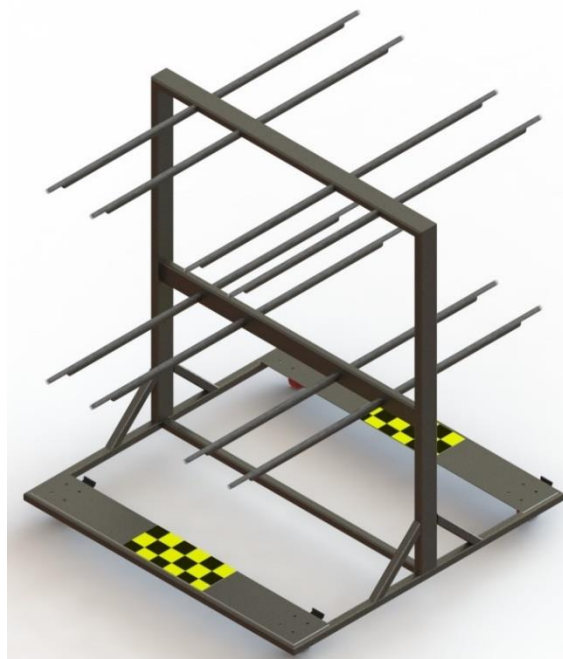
Esboço final da estrutura metálica para paletização dos painéis de porta.
